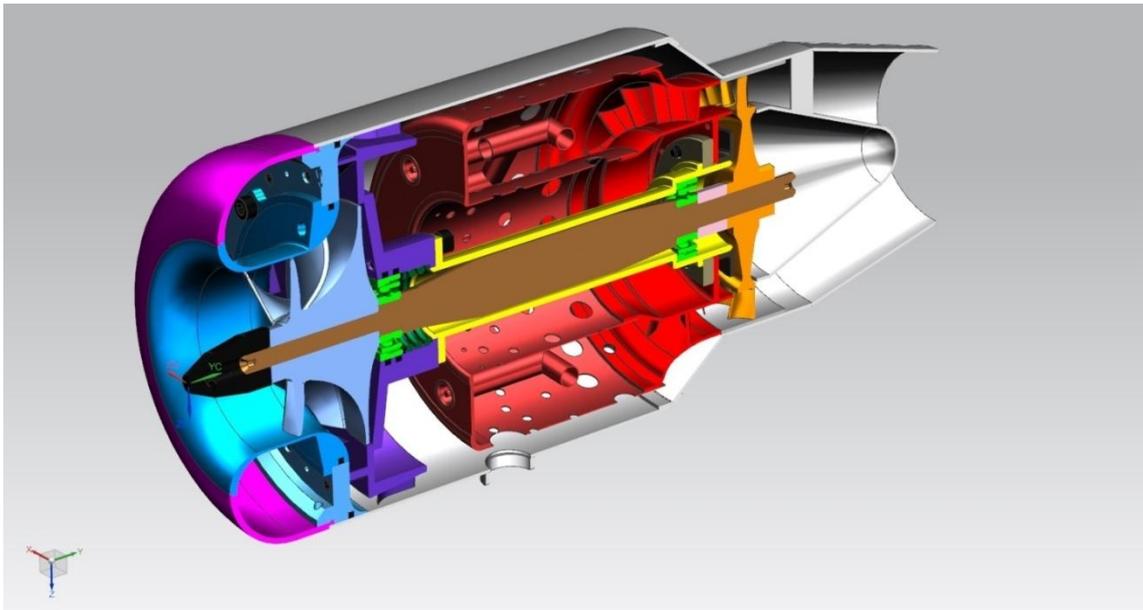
3D модель конструкции типового малоразмерного двигателя.
